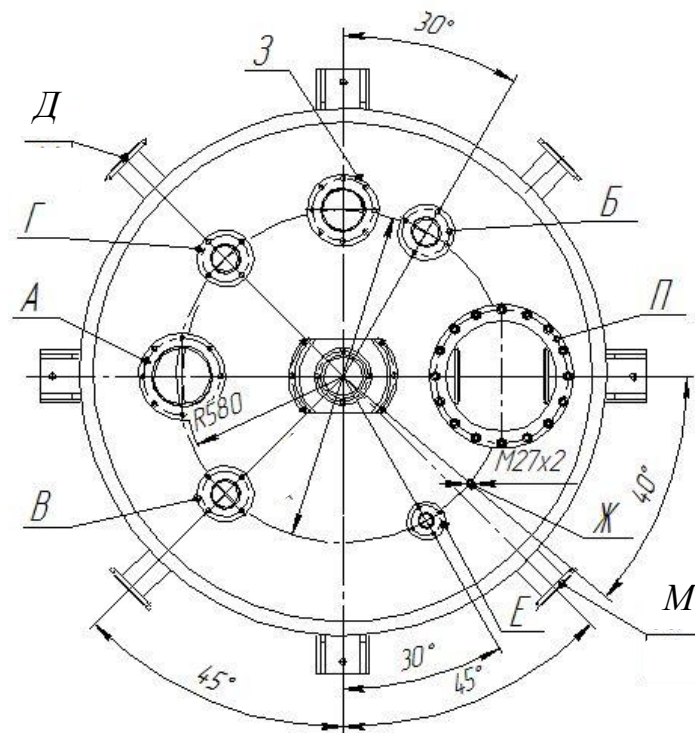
Схема расположения штуцеров, опор-лап на корпусе аппарата с эллиптической крышкой.
